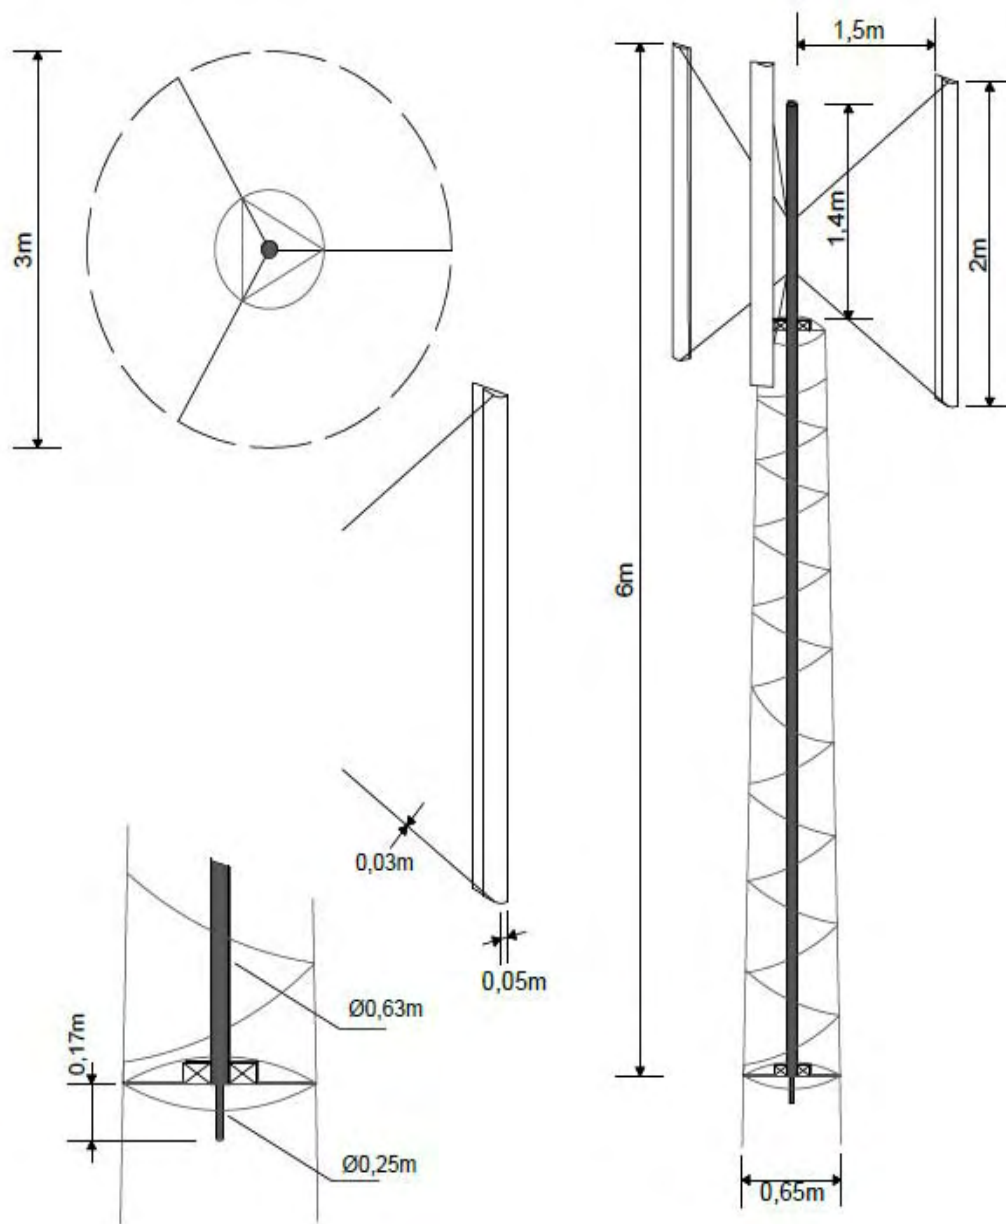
Aeromotor de eixo vertical – Dimensões principais
